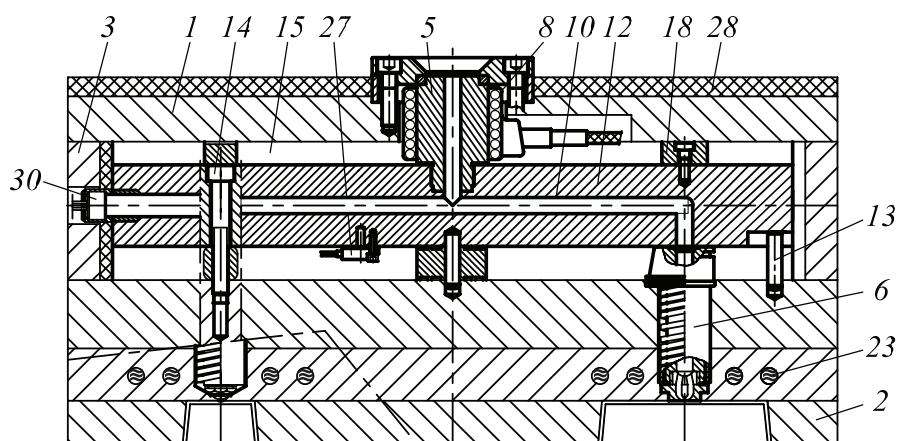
Конструкция ГКС с прямоточными соплами
